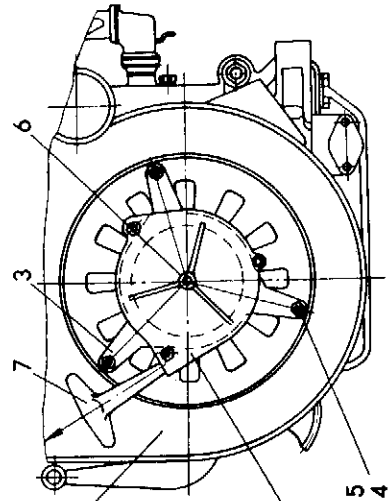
Схема установки стартера ПД-8 на двигатель:
